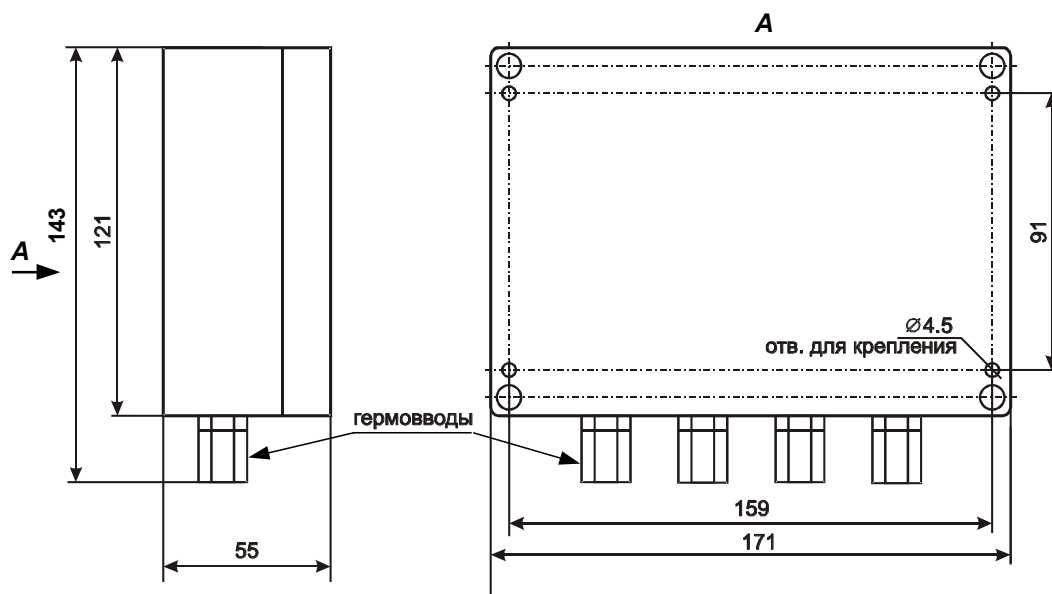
Внешний вид и габаритные размеры БРЛ в исп. IP65
